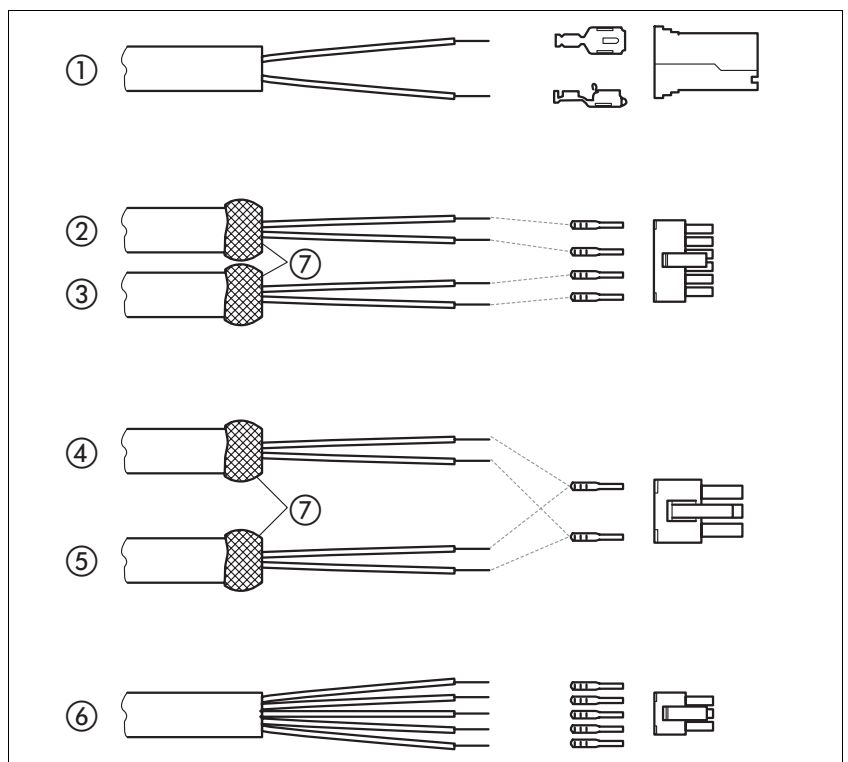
Stecker, Kabelschuhe und Crimpkontakte
